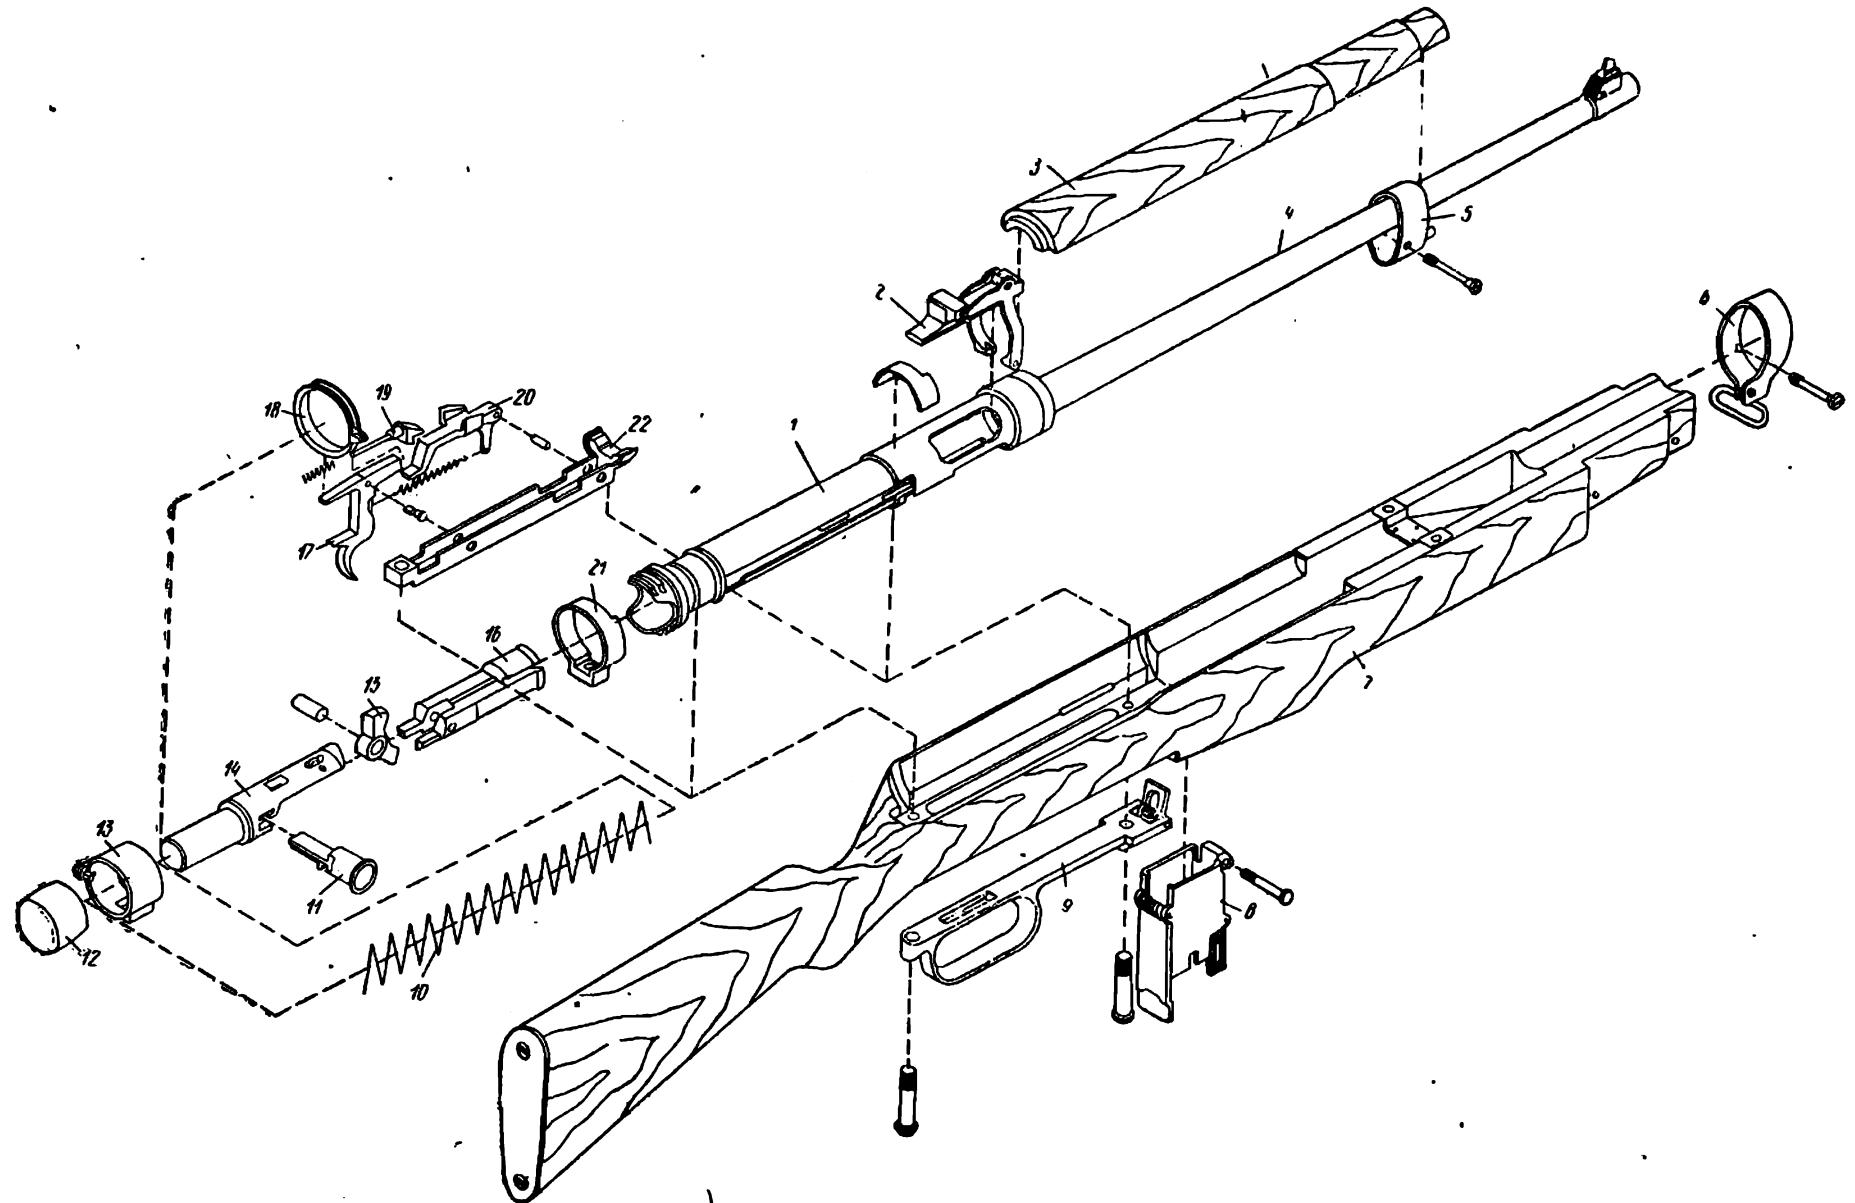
Детали и сборки автоматического карабина 39М:
